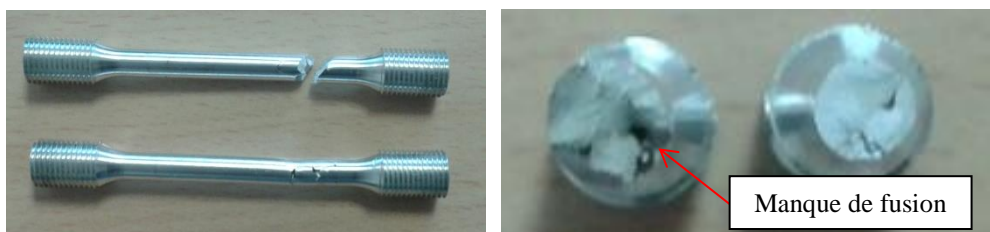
Profil et section des éprouvettes de type Talon après rupture
